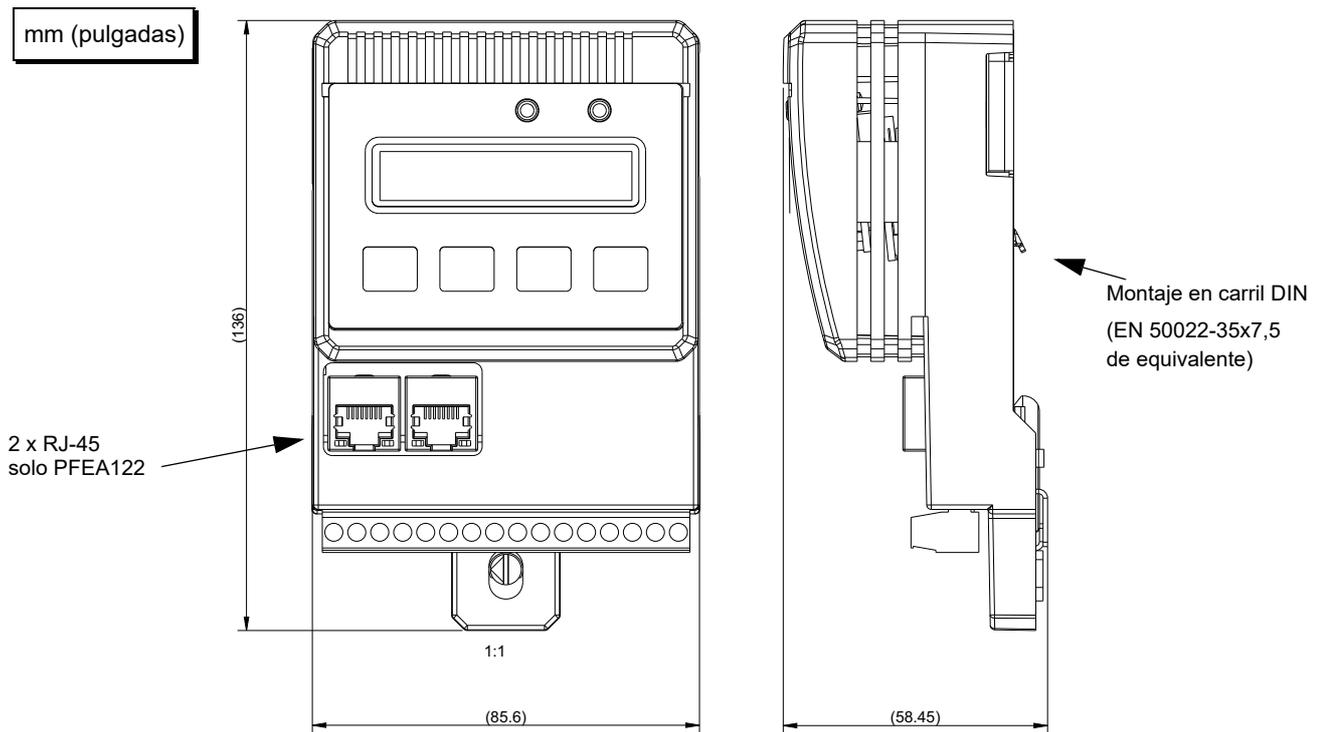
Dimensiones de instalación de la unidad PFEA122
